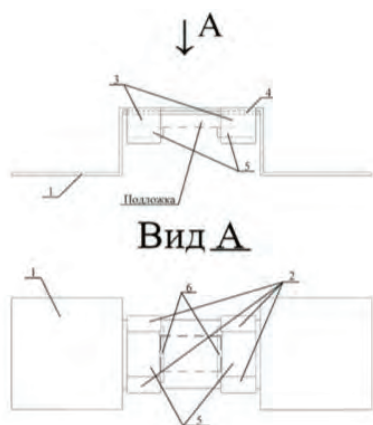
Конструкция нагреваемого держателя для образца [3]. Цифрами обозначаются следующие элементы: 1 – танталовая пластина; 2 – танталовые зажимы; 3–5 – поликорковые пластины; 6 – напускные концы
